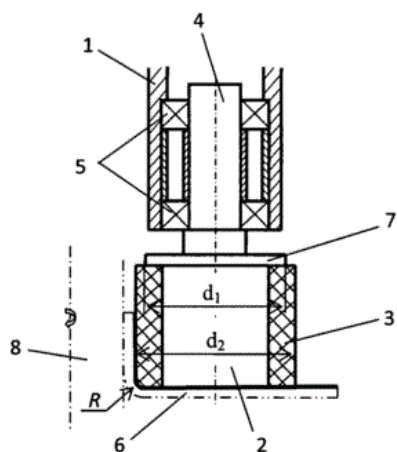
Конструкция обкатной головки: 1- державка; 2-ролик; 3-коаксиальный давящий элемент из полиуретана; 4- хвостовик; 5- радиально упорный подшипник; 6- деформируемая заготовка; 7- упорный элемент; 8- оправка
